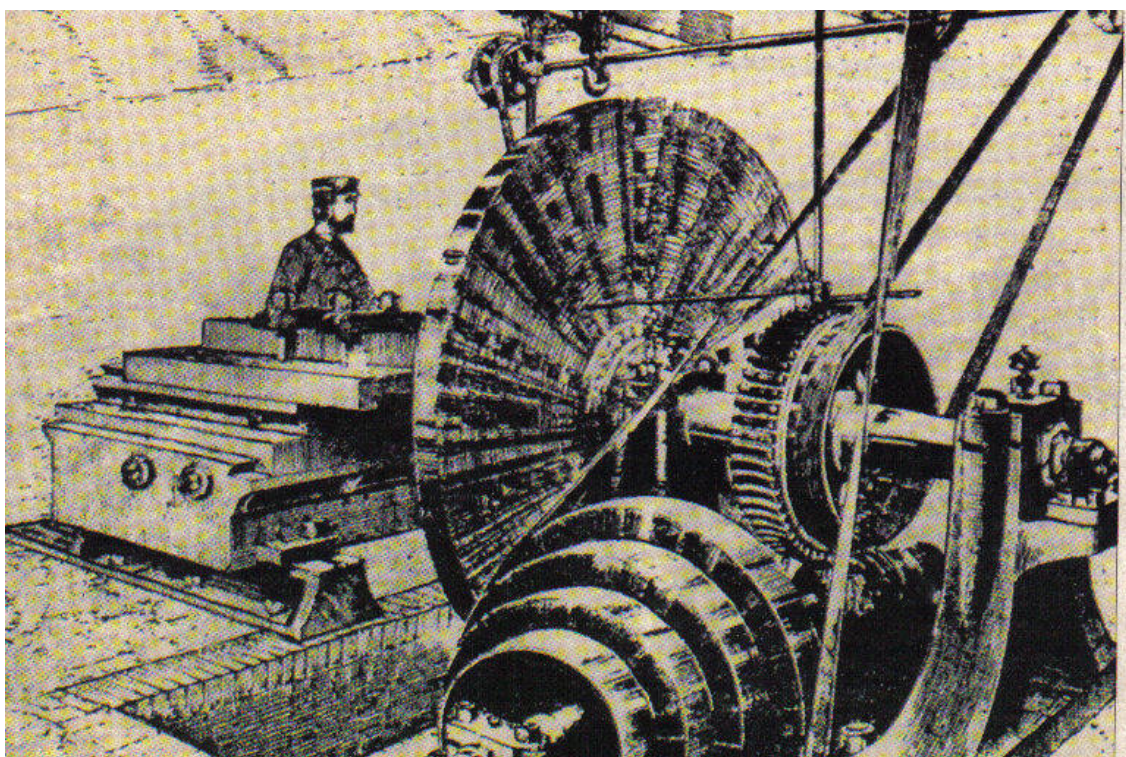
Transmisný univerzálny sústruh z r. 1862
